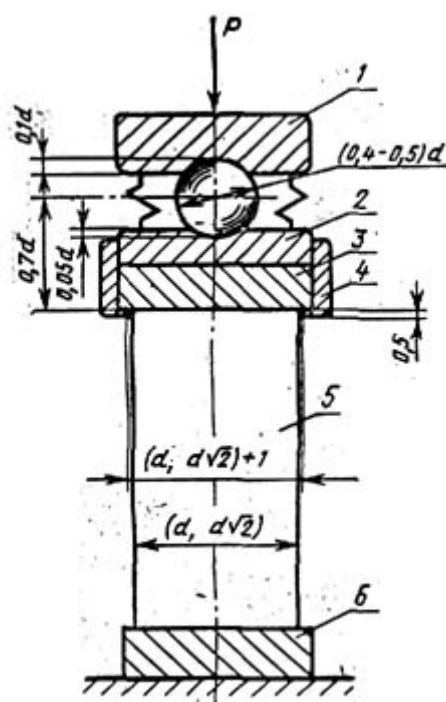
Схема приспособления для испытания на сжатие: 1 – накладная пята; 2 – подкладная пята; 3 – верхняя плита; 4 – обойма; 5 – образец; 6 – нижняя плита
